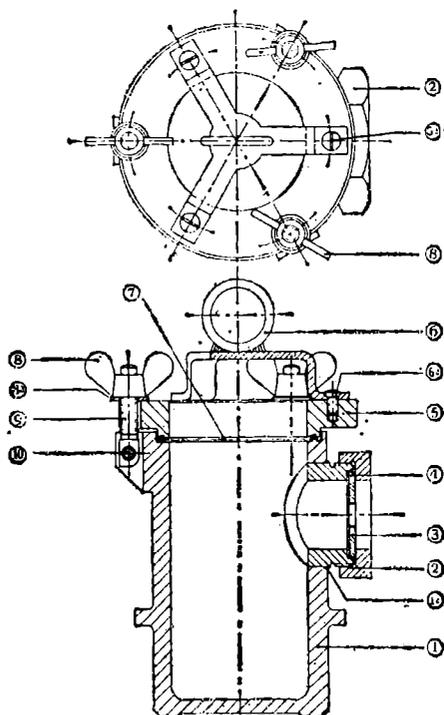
Recipiente a presión montado; vistas esquemáticas en sección vertical y en planta.
